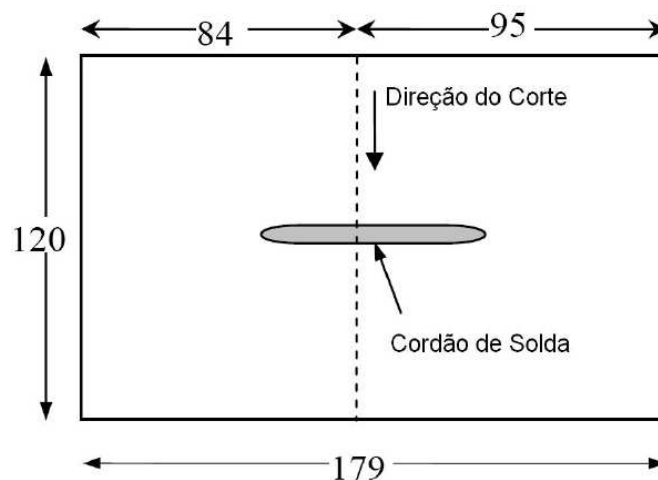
dimensões do corpo de prova e posição do corte para medição das tensões.
